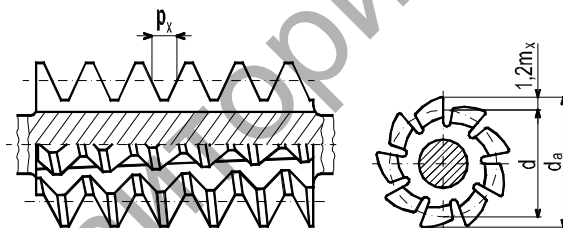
Фреза для нарезания червячного колеса с радиальной подачей [65]
